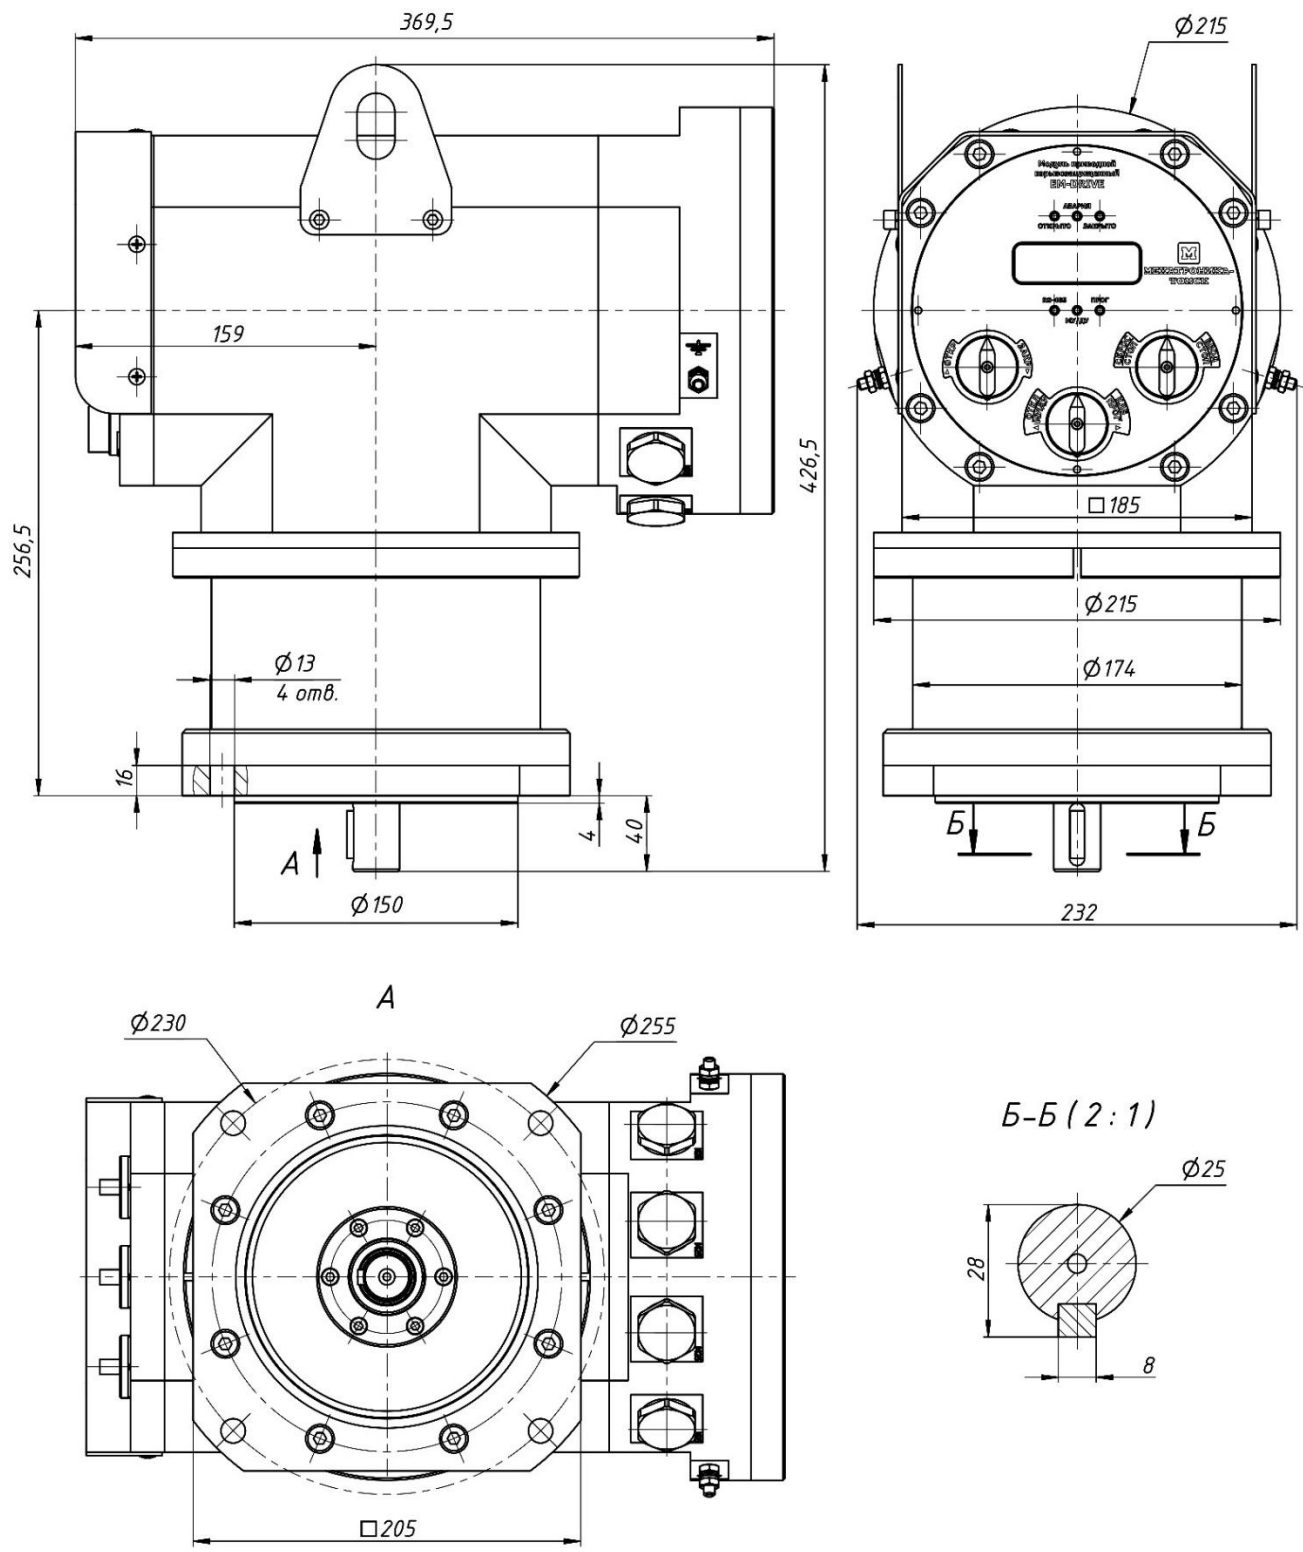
Общий вид, габаритные и присоединительные размеры модуля EM-Drive
